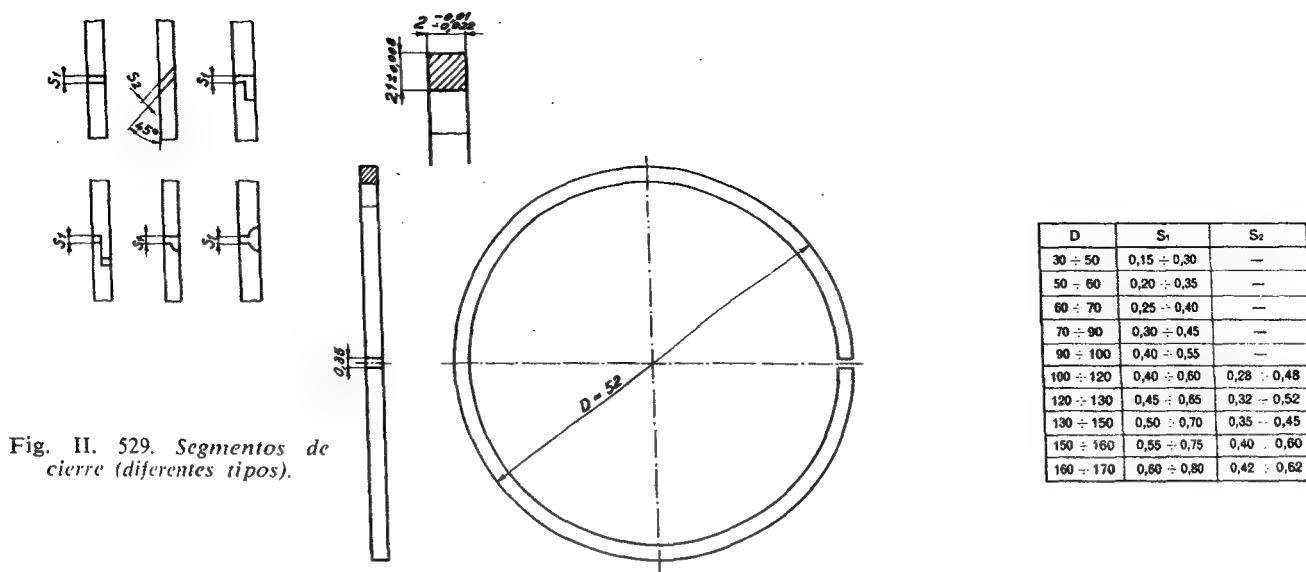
Segmentos de cierre (diferentes tipos).
